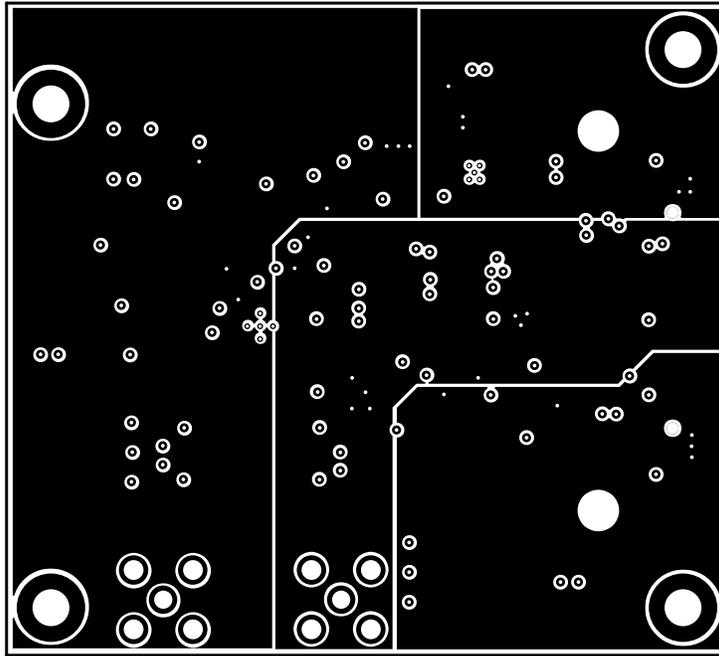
ADS8681WEVM PCB 第 3 层 - 电源平面
